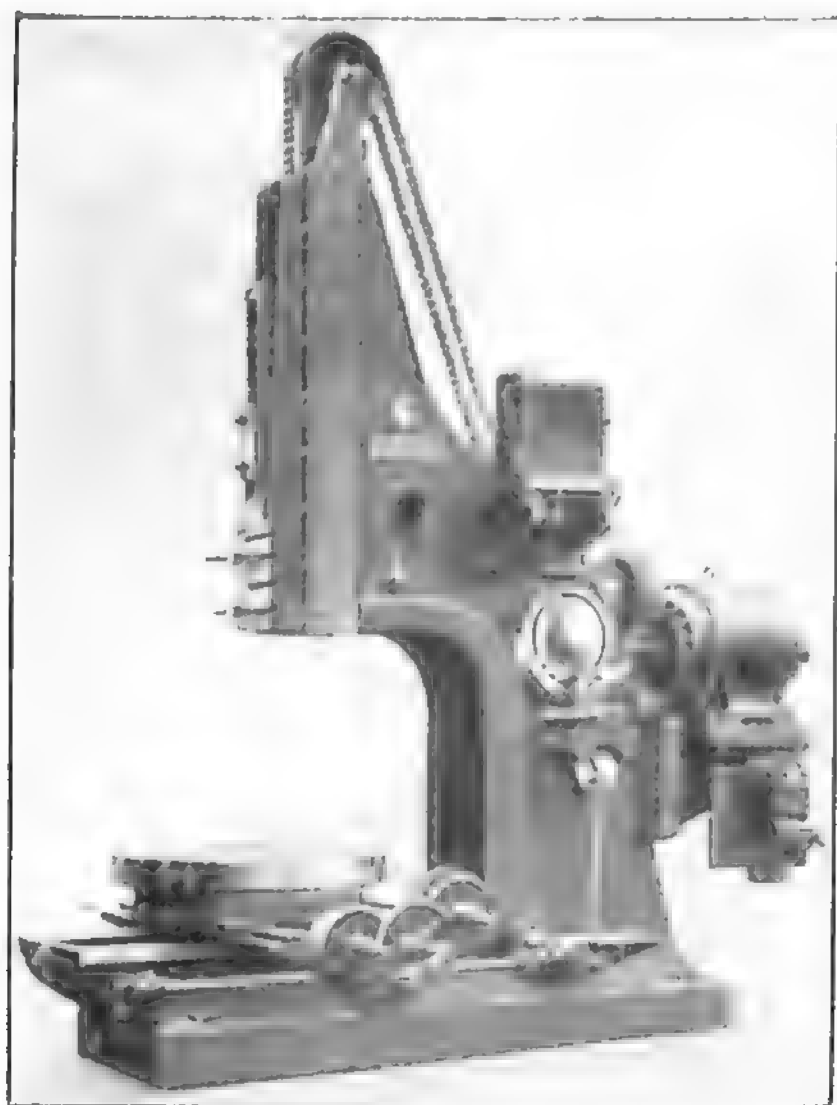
Stoßmaschine mit Umkehr-Regulier-Motor. Motor 500 oder 600 Umdr.
